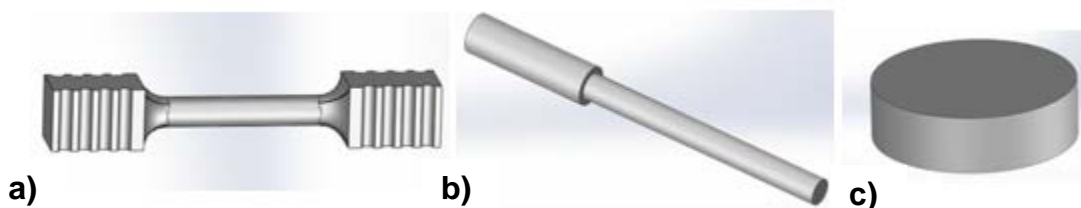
Diseño de piezas para pruebas mecánicas, a) tensión, b) fatiga y c) desgaste.
